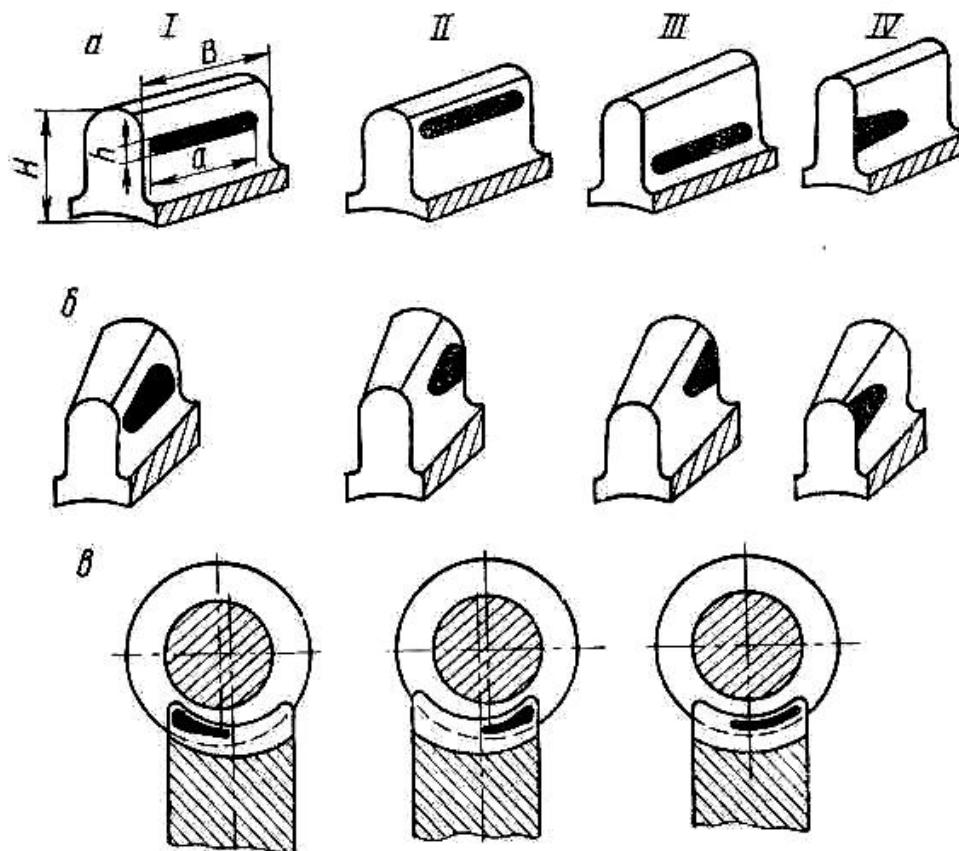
Схемы расположения пятен контакта зубьев: а — цилиндрической передачи; б — конической передачи; в — червячной передачи
